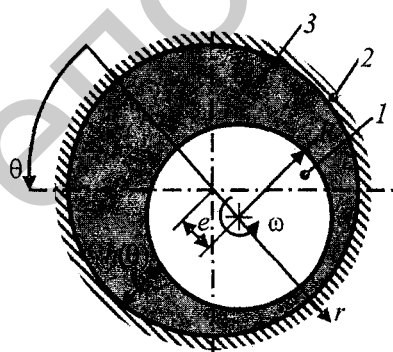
Поперечное сечение подшипника (полярный угол θ отсчитывается от точки минимума толщины смазочного слоя против часовой стрелки): 1 — вал; 2 — немагнитная обечайка подшипника; 3 — смазка
